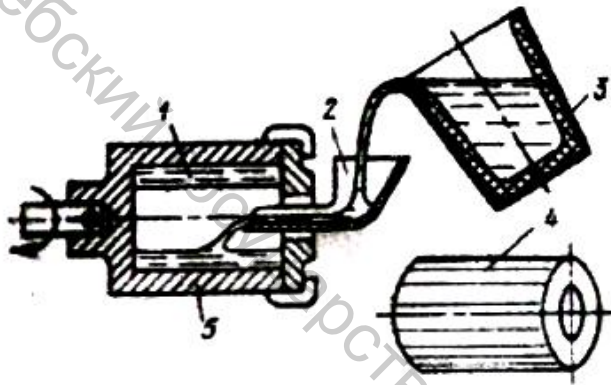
Схема получения отливки при вращении формы вокруг горизонтальной оси: 1- расплав, 2- заливочный желоб, 3- ковш, 4- отливка, 5- вращающаяся форма
